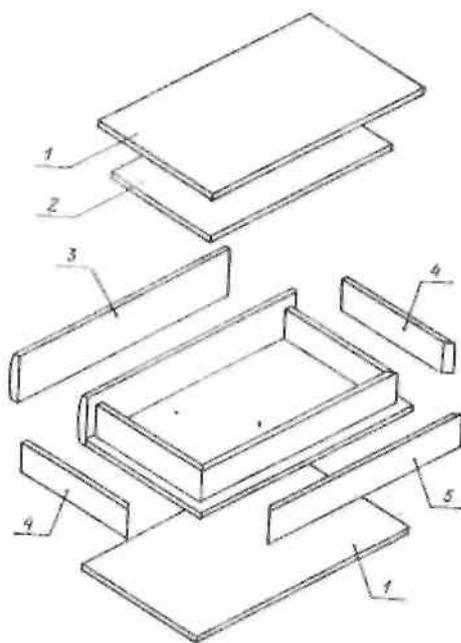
Шкатулка-книга: 1 - "корочки" (2 шт.); 2 - направляющая крышки (приклеивается к детали 1); 3 - "корешок"; 4 - боковые стенки ("страницы"); 5 - передняя стенка.
